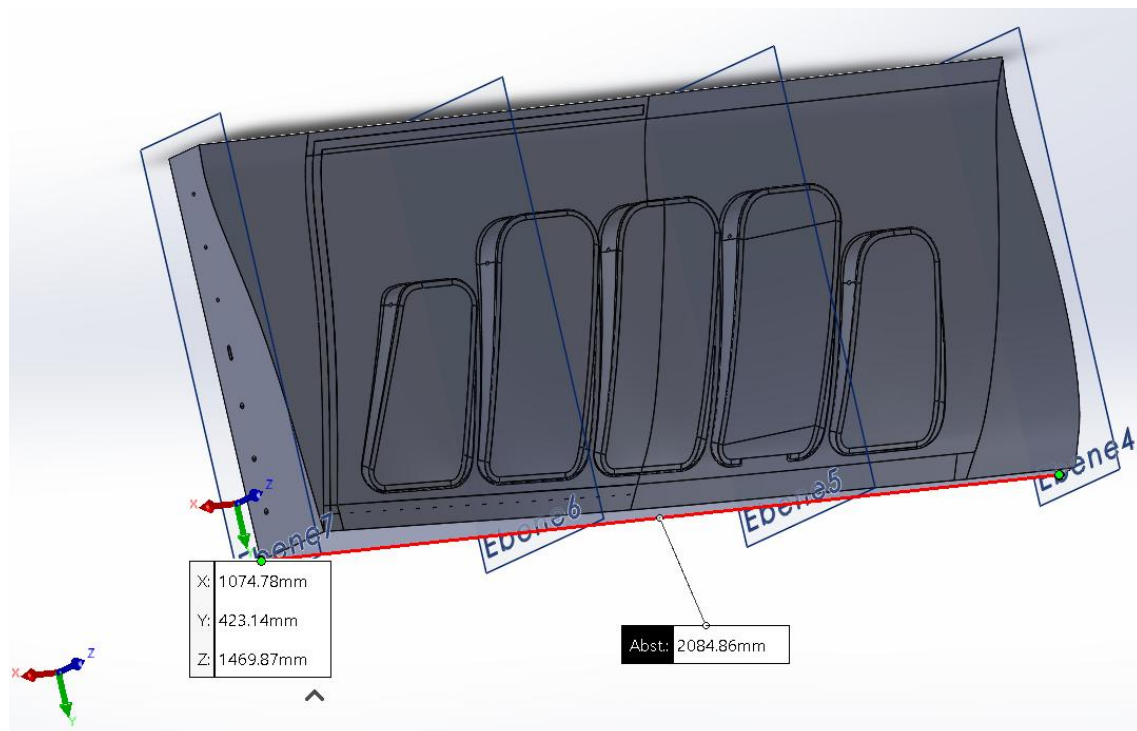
Formwerkzeug zur Herstellung der Unterseite des Segmentes der Flugwindkraftanlage.
